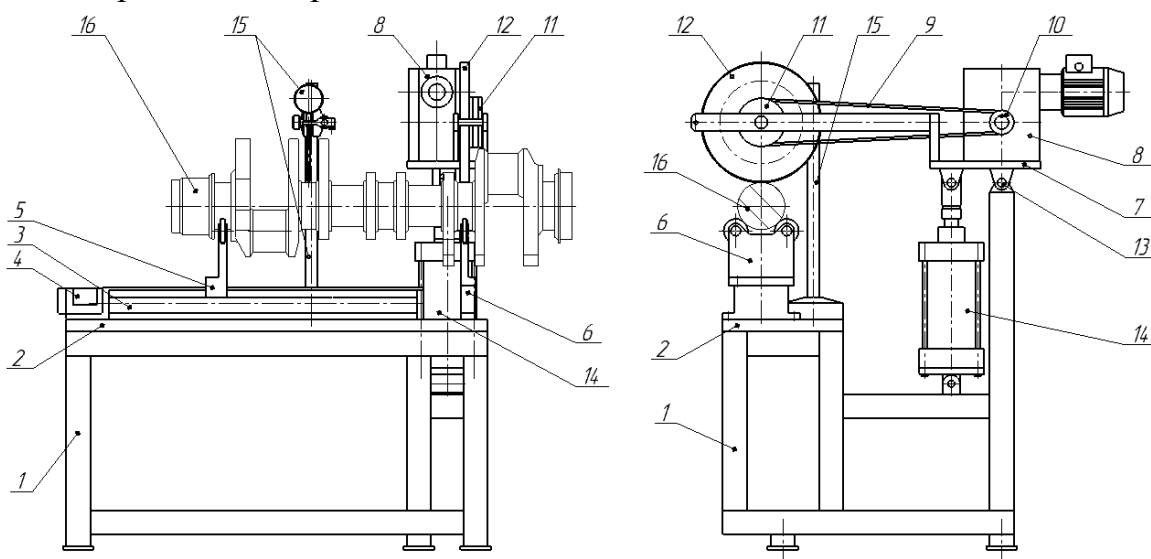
Стенд для контроля биения коренных шеек коленчатого вала
